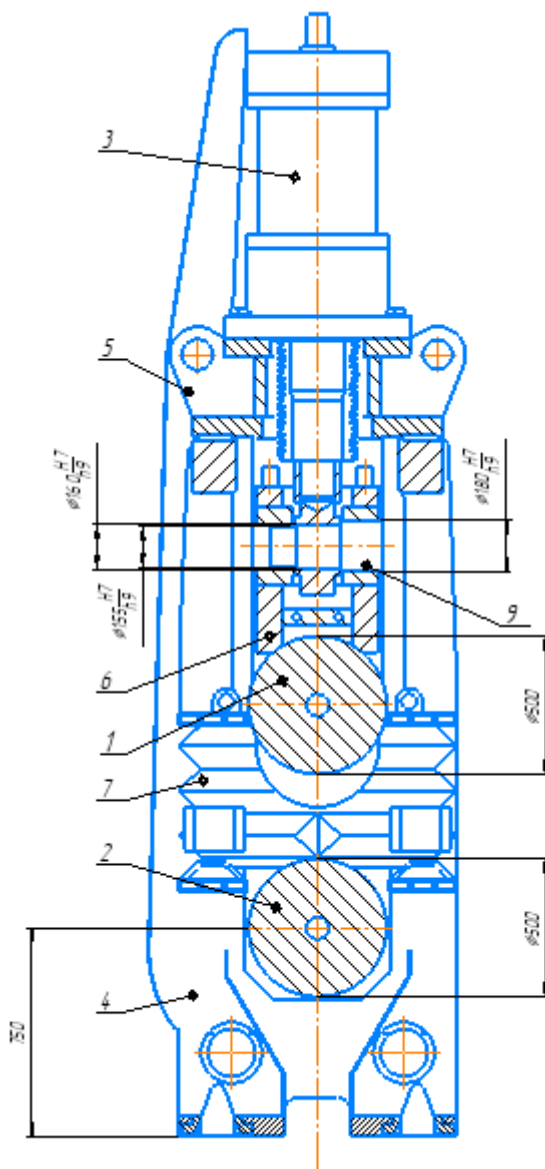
Тянуще-правильный агрегат : 1 – приводной ролик; 2 - холостой ролик; 3 – гидроцилиндр; 4 – станина; 5 – фланец; 6 – прижимной механизм; 7 – рубашка охлаждения; 8 – мотор-редуктор; 9 – палец гидроцилиндра
